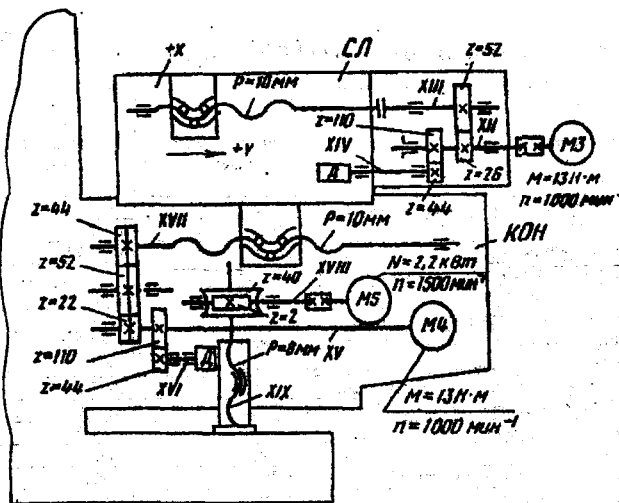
Кінематична схема хрестового столу фрезерного верстата мод. 6P13Ф3
